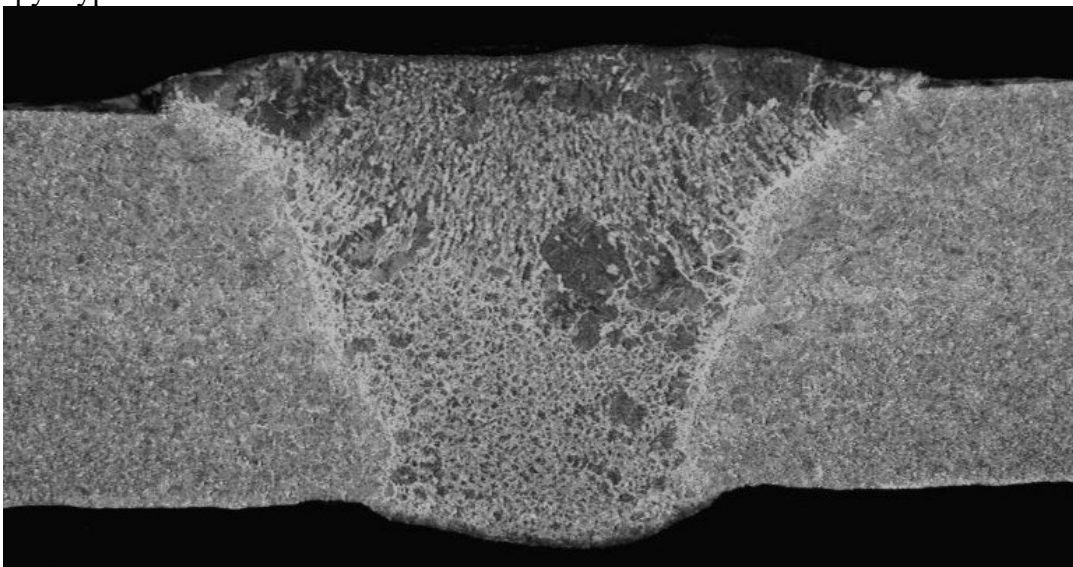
Способ сварки 111. Стыковой шов. (22)
